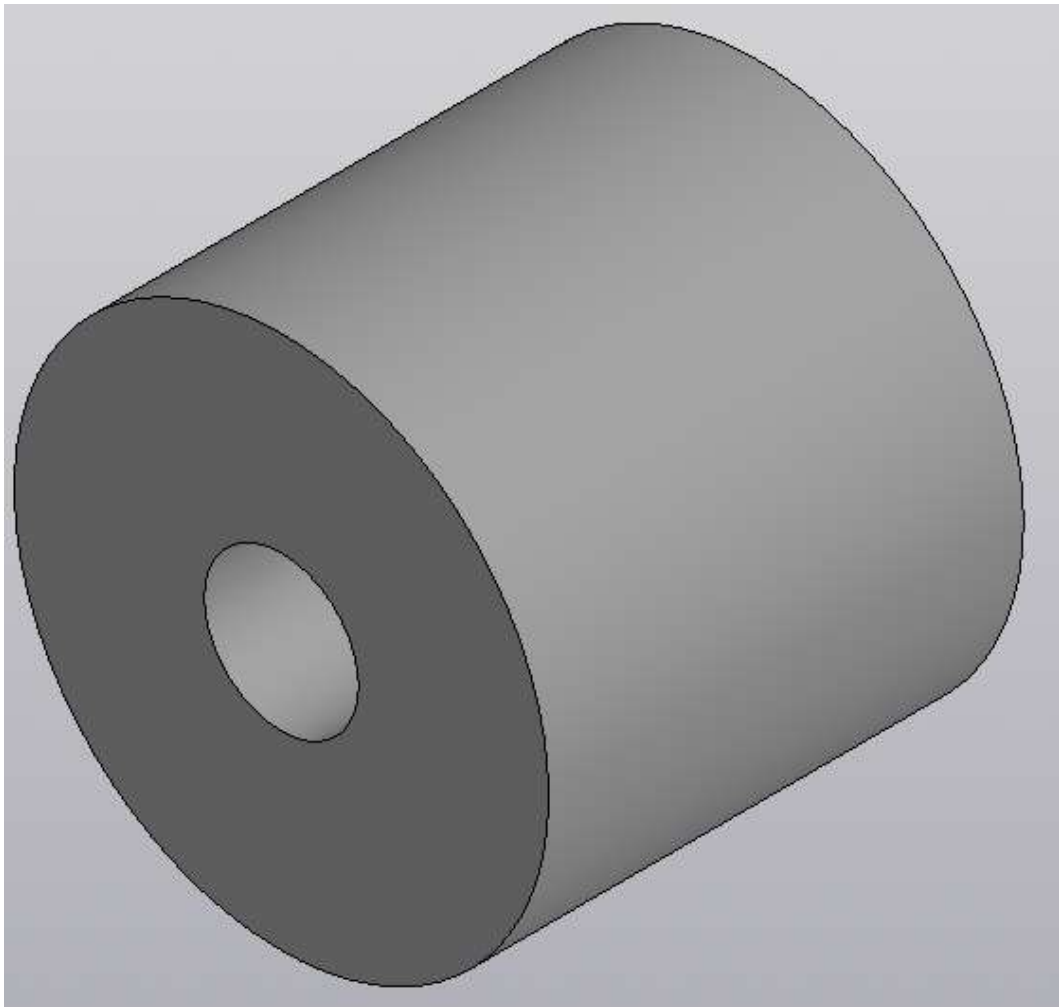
3-D- модель заготовки деталі «оптичний дефлектор»
